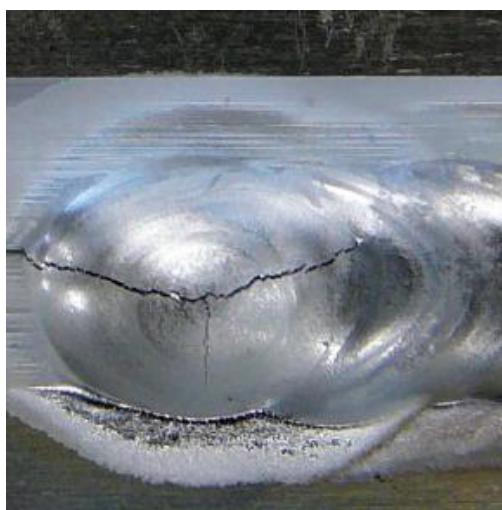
Растрескивание сварочного шва после сварки алюминиевого сплава [7]
